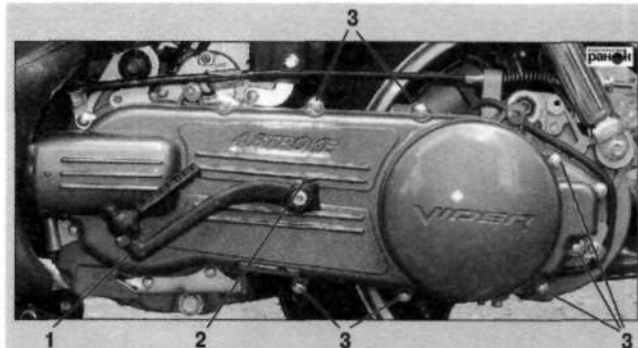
Крышка вариатора: 1 – рычаг кикстартера; 2 – болт крепления рычага кикстартера; 3 – болты крепления крышки вариатора
